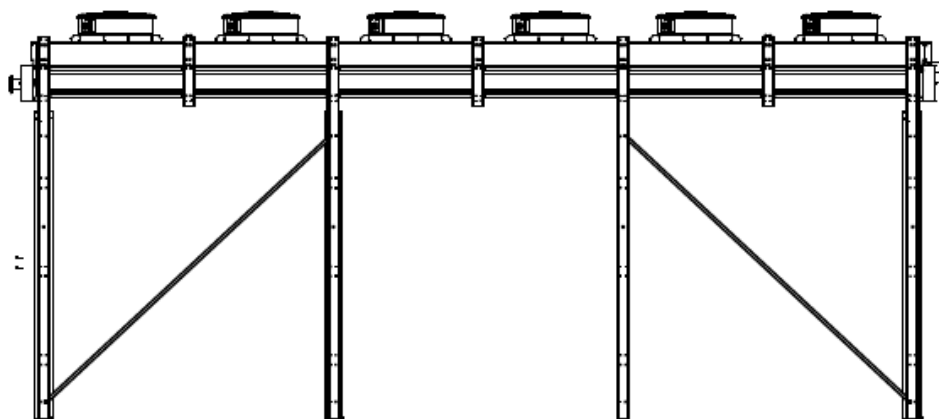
Instalación de la pata de montaje elevado (Serie AlfaSolar SR™)
